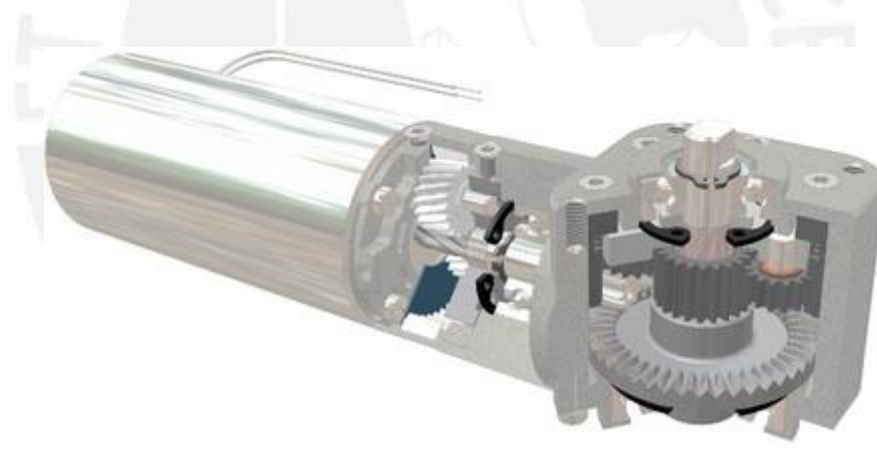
Vista en sección de un motor EC con reductor de engranajes tipo corona⁴¹
